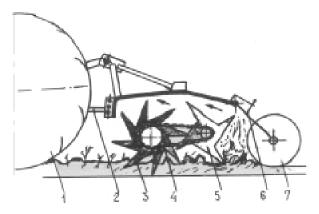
Схема ротационной ножевой бороны РБР-4: 1 — трактор; 2 — навеска трактора; 3 — зубовый ротор; 4 — цепная передача; 5 — ножевой ротор; 6 — механизм регулировки глубины; 7 — каток
